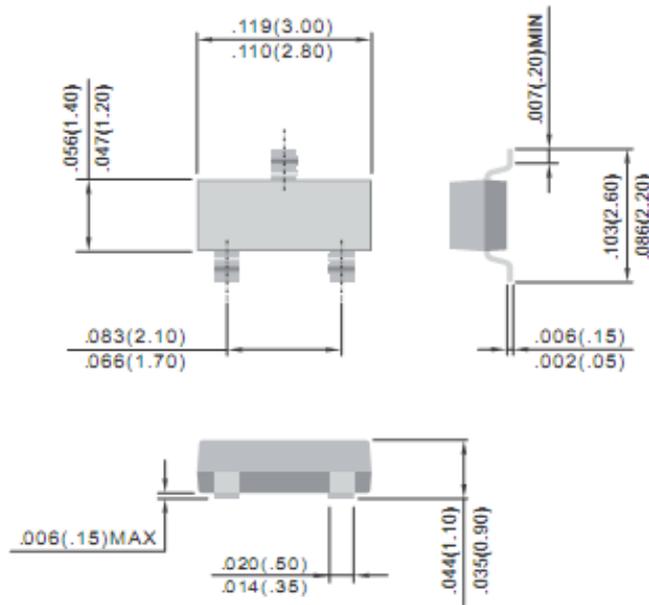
Габаритные и установочные размеры корпусов типа SOT-23
